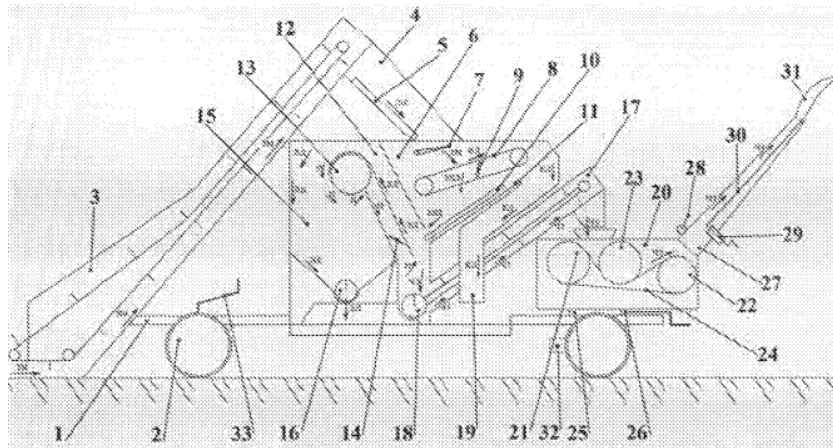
Очисник вороху самопересувний-зернометальник: 1 – рама; 2 – колеса; 3 – завантажувальний транспортер вороху; 4 – відвантажувальний патрубок; 5 – розподілюючі ребра; 6 – зерноочисний блок; 7 – поворотна площадка; 8 – ланцюговий транспортер(сітчастий); 9 – підбивальник; 10 – жолобчастий розподільник; 11 – скатна поверхня; 12 – пневмосепаруючий канал; 13 – діаметральний вентилятор; 14 – повітряна заслінка; 15 – осадова камера; 16 – шнек легких відходів; 17 – відвантажувальний транспортер; 18 – живильники; 19 – бункер крупних відходів; 20 – відвантажувальний тример; 21 – натяжний барабан; 22 – приводний барабан; 23 – активна котушка; 24 – нескінченна ребриста стрічка; 25 – гальмівний барабан; 26 – стрічково-гвинтове гальмо; 27 – труба тримера; 28 – лебідка тросова; 29 – гвинтова пара.
